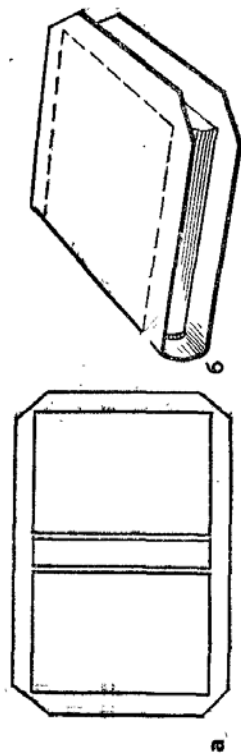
Изготовление цельнокрытой переплетной крышки:
